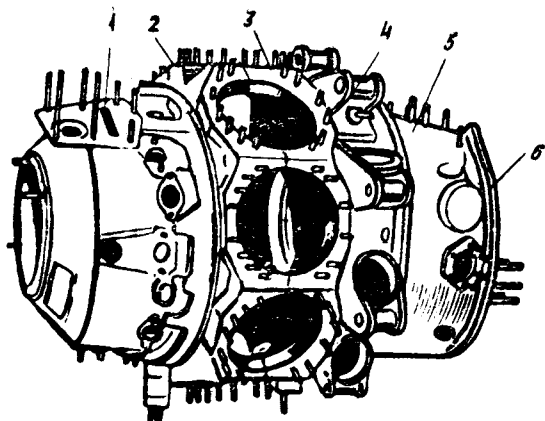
Картер двигателя: 1 — носок картера; 2 — передняя часть среднего картера; 3 — задняя часть среднего картера; 4 — передний корпус нагнетателя; 5 — задний корпус нагнетателя; 6 — задняя крышка
